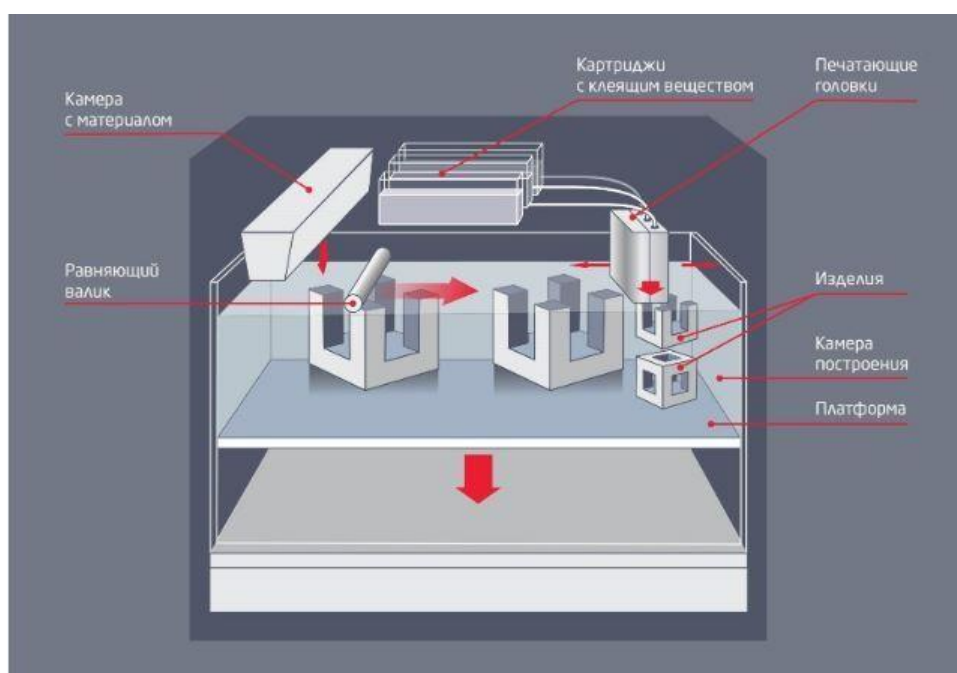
ColorJet Printing: конструкция 3D-принтера
